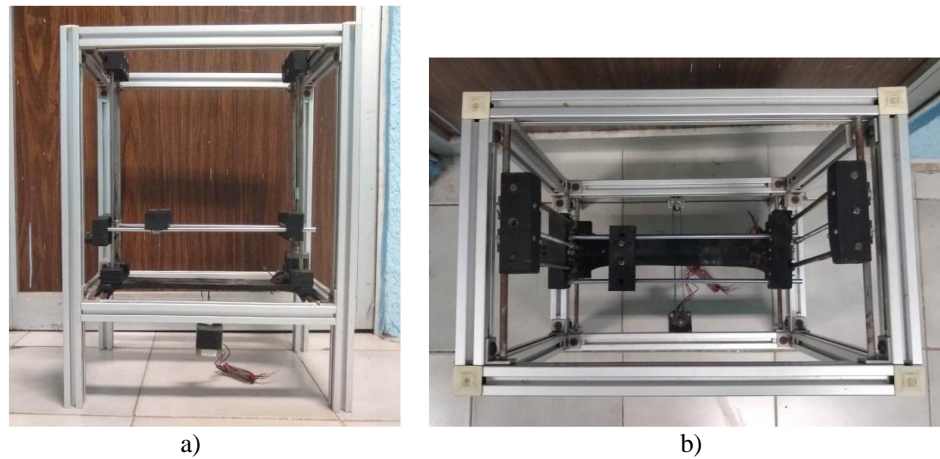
Vista de la estructura. a) Frontal. b) Superior.
